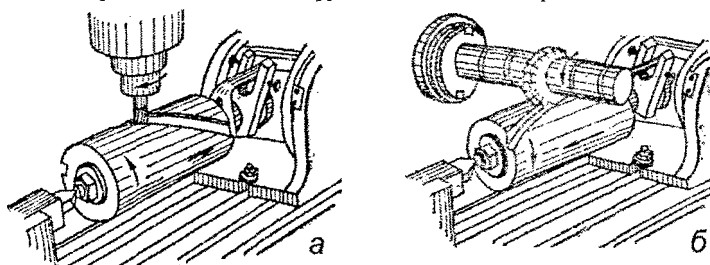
Образование винтовой канавки на вертикально-фрезерном (а) и горизонтально-фрезерном (б) станках
